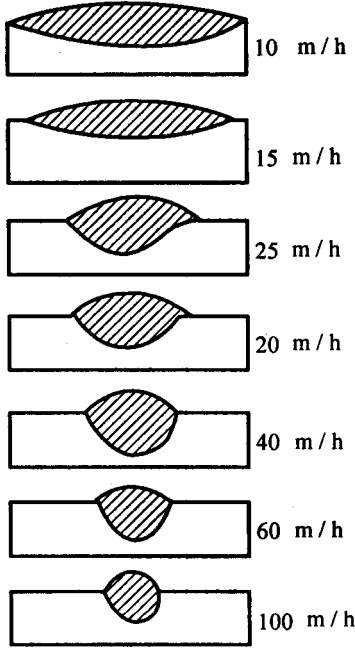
焊接速度对焊缝成形的影响
